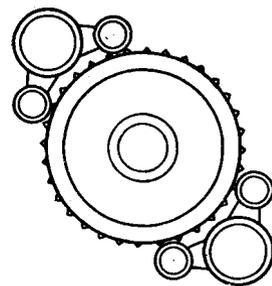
Комбинированный зубчатый барабан с прижимными каретками
